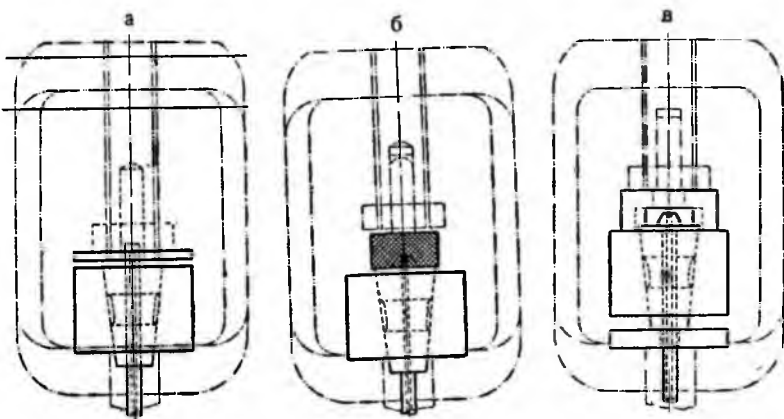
Порядок операций по обсадке трубок высокого давления: а — закрепление трубки, б — обсадка головки, в — выпрессовка разрезной гильзы.
